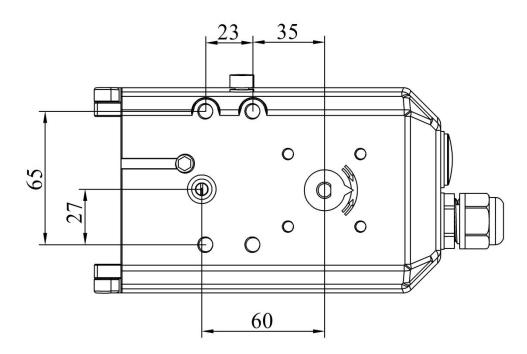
Взаимное расположение соединительных отверстий и отверстий для крепления установки без трубопроводов
